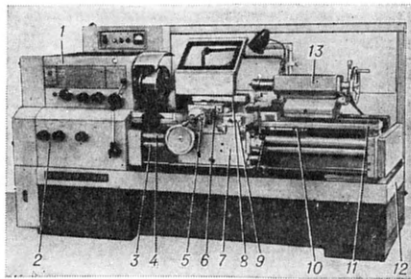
Универсальный токарно-винторезный станок производства завода «Красный пролетарий» (модель 16К20): 1 — передняя бабка; 2 — коробка подач; 3 — ходовой валик; 4 — ходовой винт; 5 — винт подачи поперечных салазок; 6 — поперечные салазки; 7 — фартук; 8 — верхняя каретка; 9 — каретка суппорта; 10 — рейка; 11 — станина; 12 — основание; 13 — задняя бабка.
